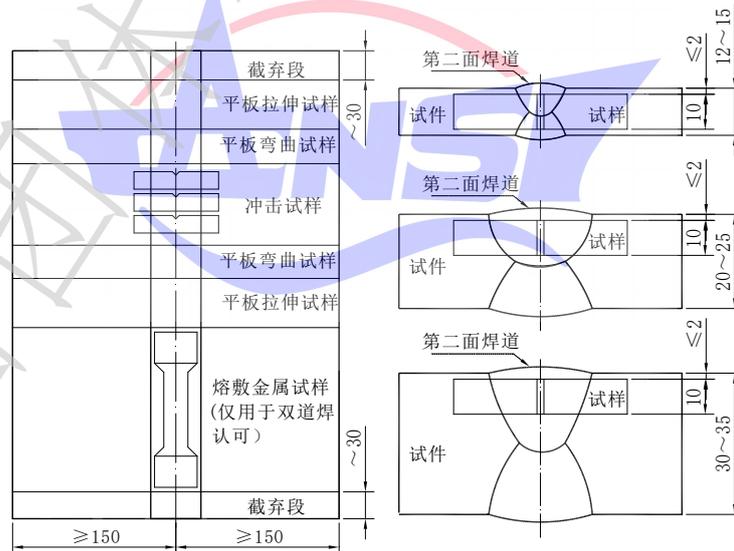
埋弧双面单道焊工艺试件的取样位置
